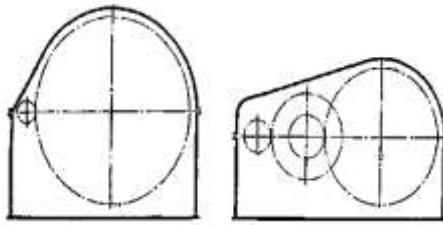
Сопоставление габаритов одноступенчатого и двухступенчатого редукторов с цилиндрическими колесами при одинаковом передаточном числе $i = 8,5$
